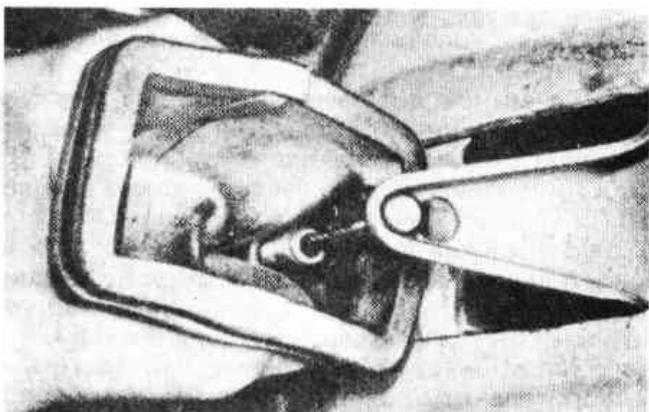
Извлечение чехла троса сцепления из корпуса (Разд.6)
